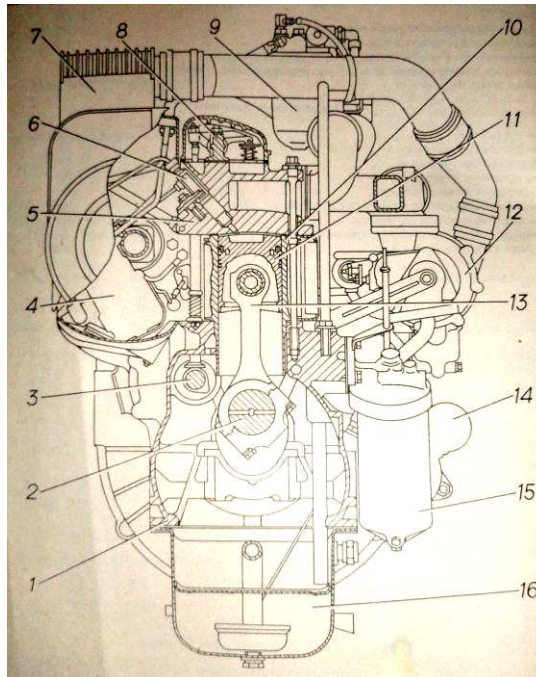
Поперечний розріз двигуна: 1 – картер двигуна; 2 – колінчастий вал; 3 – розподільний вал; 4 – паливний насос високого тиску; 5 – голівка циліндра; 6 – форсунка; 7 – охолоджувач наддувного повітря; 8 – привод клапанів; 9 – паливний фільтр; 10 – циліндр; 11 – поршень; 12 – турбокомпресор; 13 – шатун; 14 – стартер; 15 – мастильний фільтр; 16 – мастильний картер
